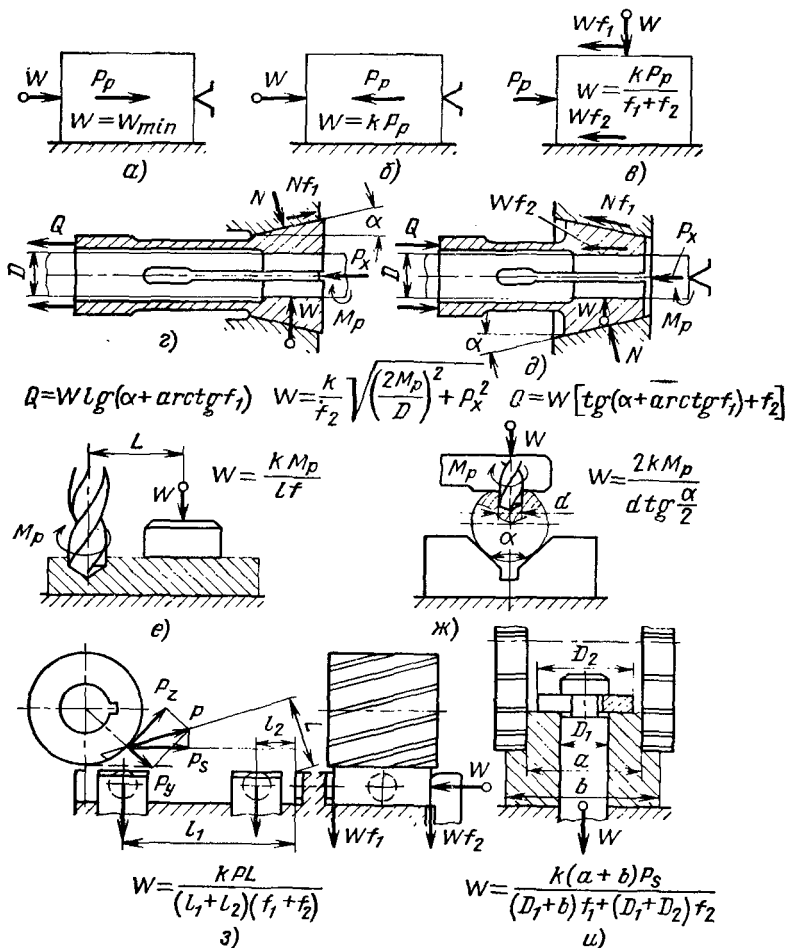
Схемы закрепления заготовок в приспособлениях и формулы для определения потребных усилий зажима:
